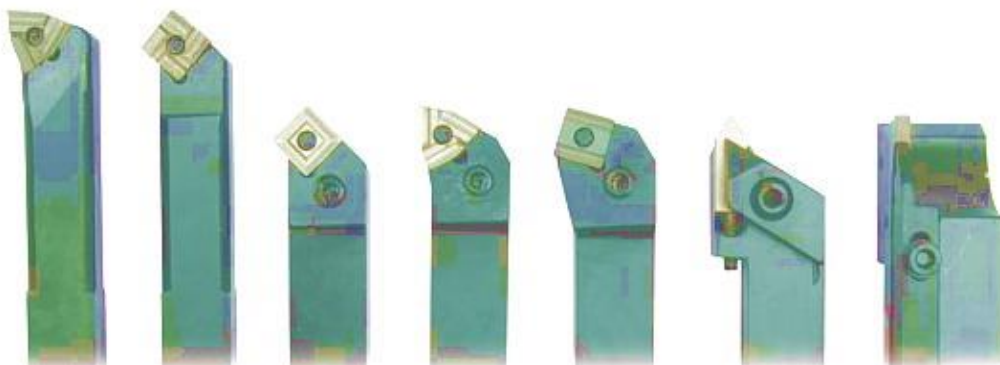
Токарные резцы с пластинами твёрдого сплава
